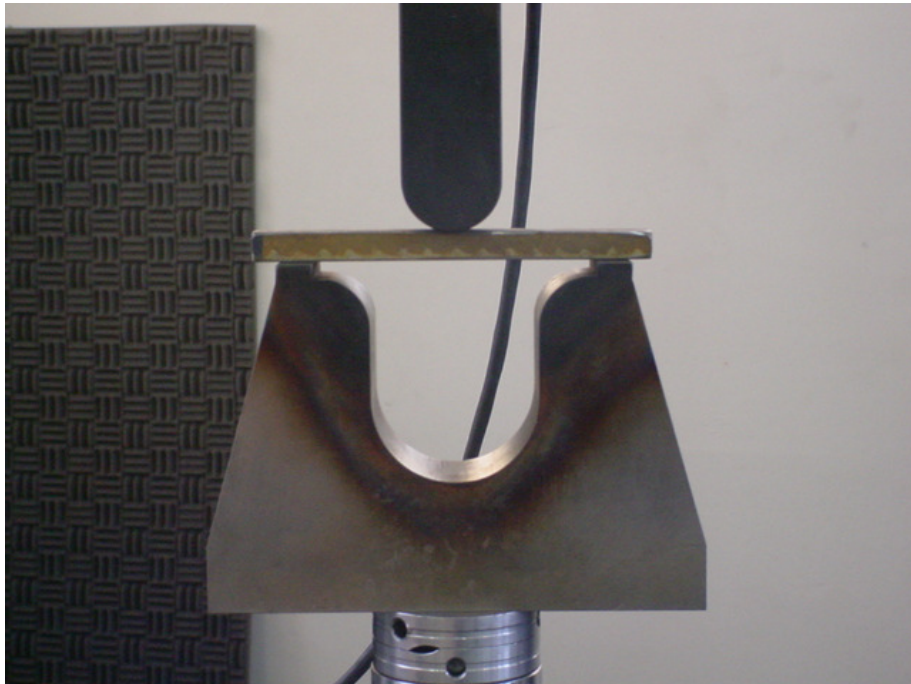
Corpo de prova posicionado no dispositivo de dobramento.
